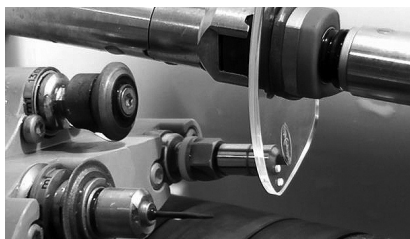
Гравировка очковой линзы на обрабатывающем станке Essilor Mr Blue 2.0
